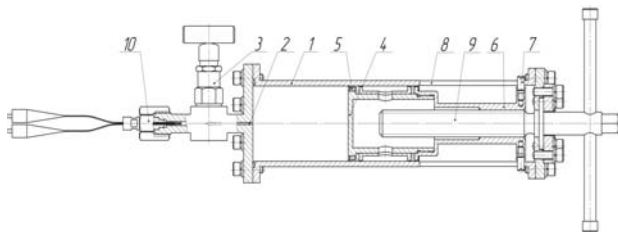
Общий вид разработанного компримирующего устройства: 1 – корпус с отверстием 2 для подачи газа; 3 – запорный элемент; 4 – поршень; 5 – эластичное уплотнение; 6 – гайка; 7 – штифт; 8 – продольные прорези; 9 – винт; 10 – оптический зонд
